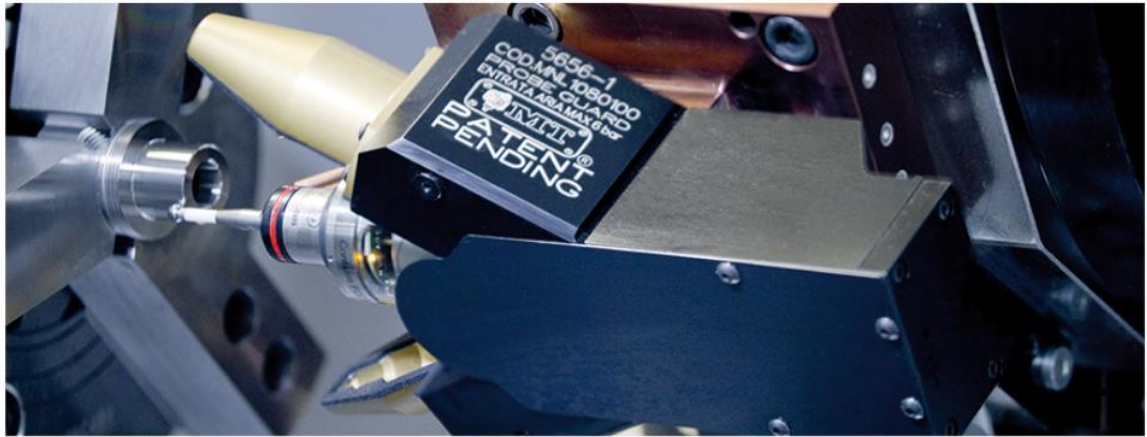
Пристрій для захисту вимірювальних інструментів - MT-TPS Touch Probe Shield
